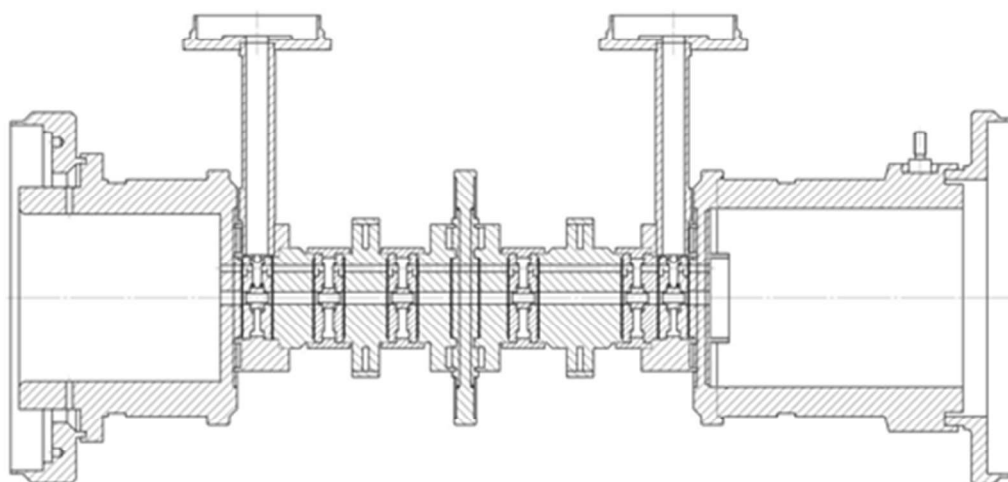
Эскиз резонаторного блока клистрона КИУ-283
